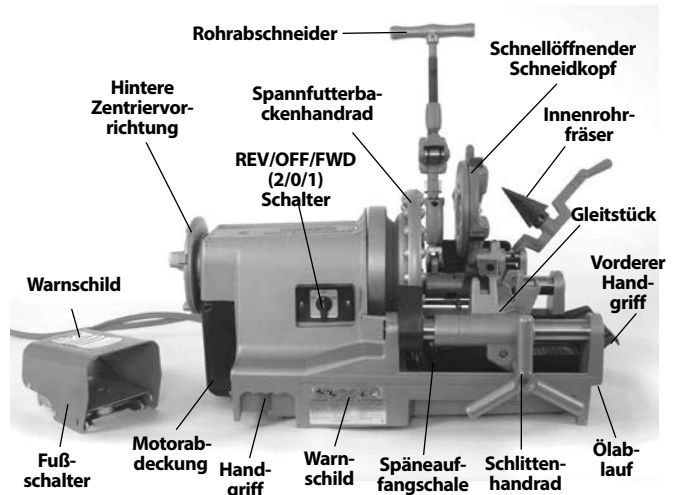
300 Compact Gewindeschneidmaschine
